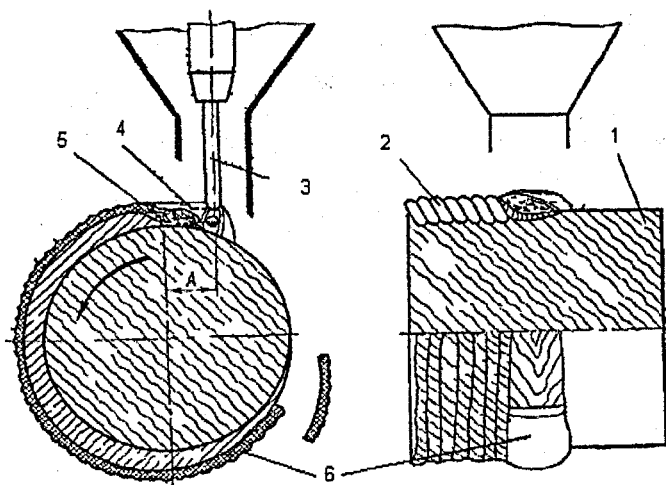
Схема автоматичного наплавлення під флюсом: 1— основний метал; 2 — наплавлений метал; 3— електрод; 4 — розплавлений метал; 5 — флюс; 6 — шлакова кірка; А — зміщення електрода із zenіту
